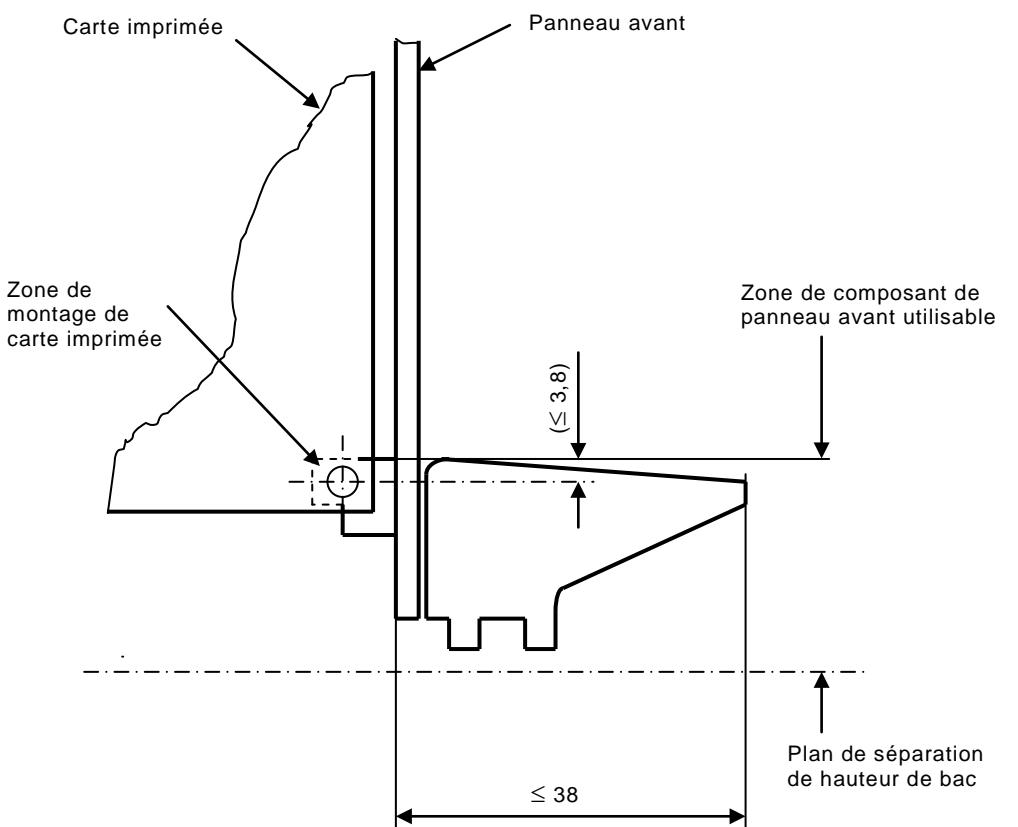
Dimensions d'interface de bac pour injecteur/extracteur monté sur panneau avant, Type A
